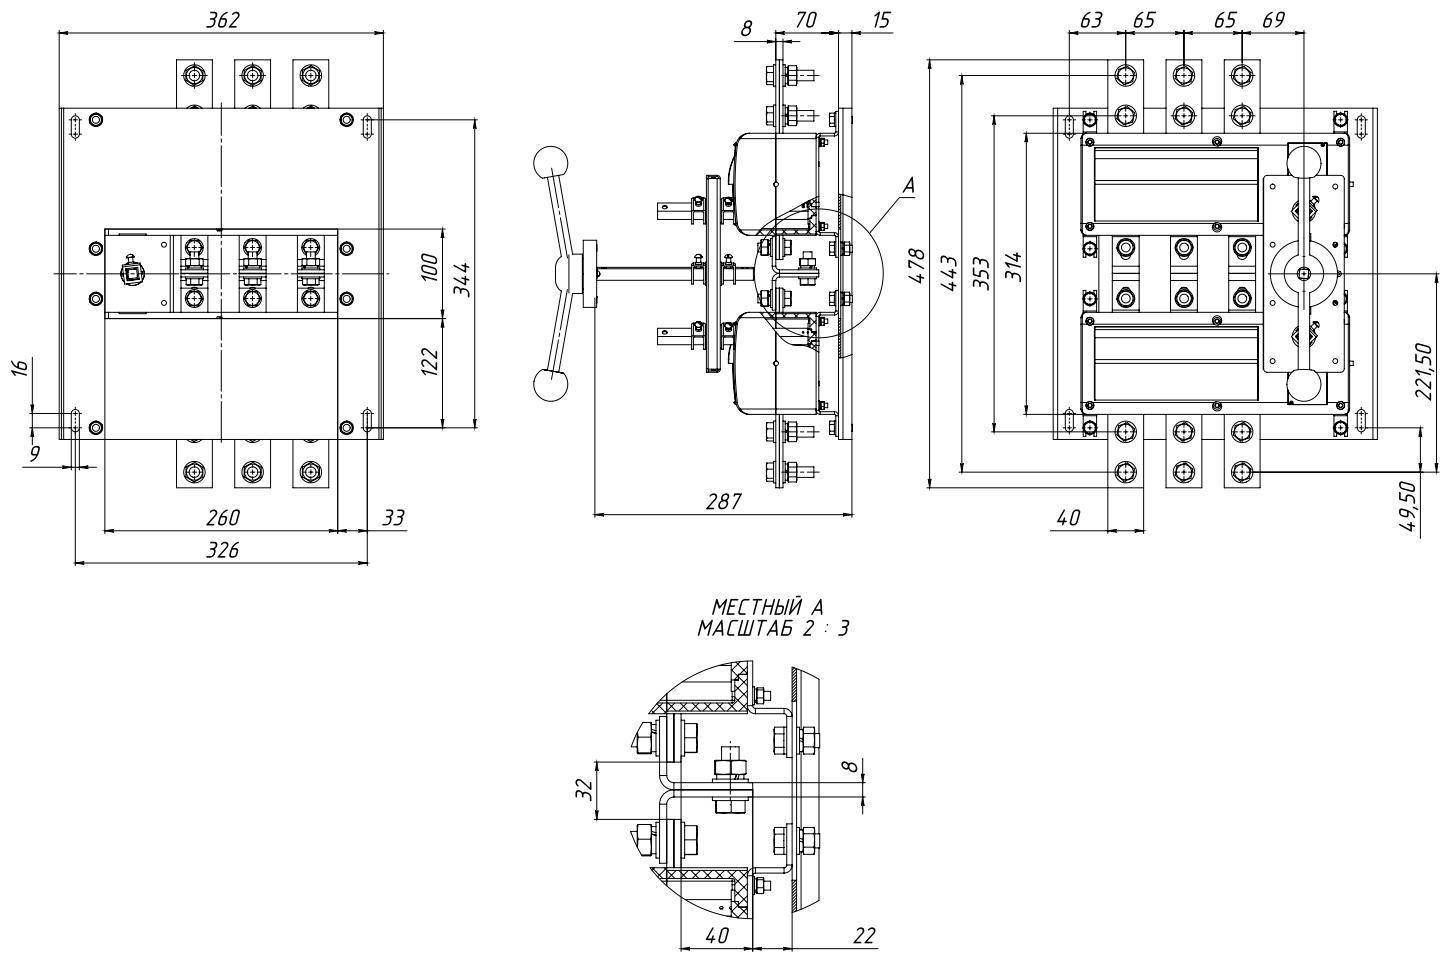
Выключатель-разъединитель ВНК-39-71130-32 УХЛЗ
